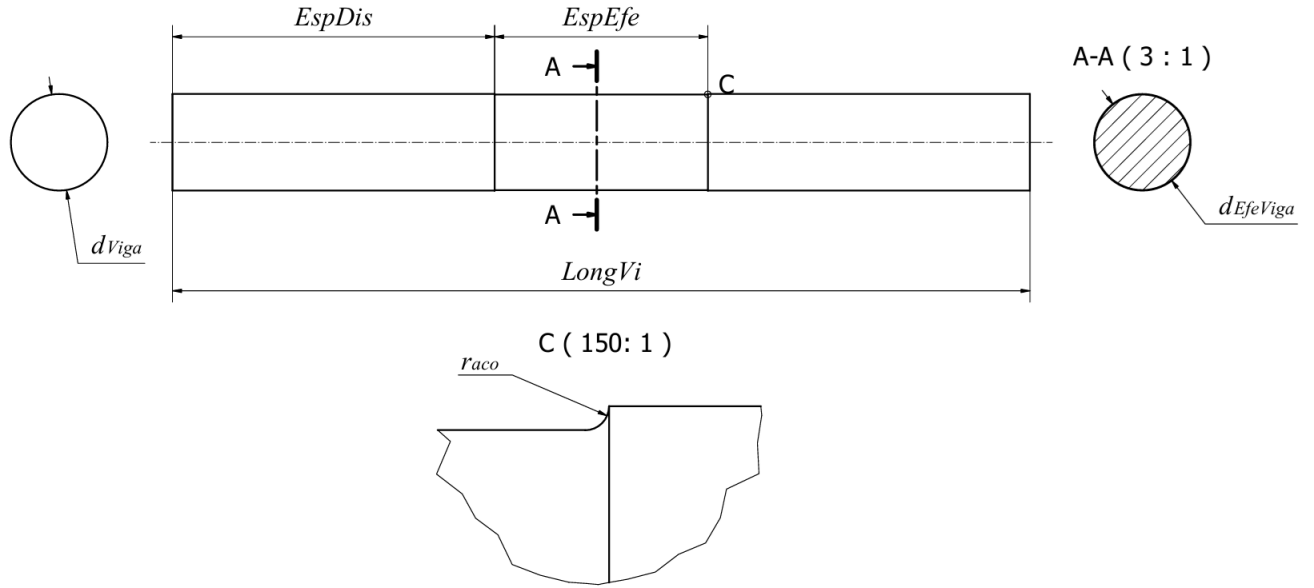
Descripción geométrica de las vigas encargadas de soportar y permitir el movimiento de los engranajes planetarios.
